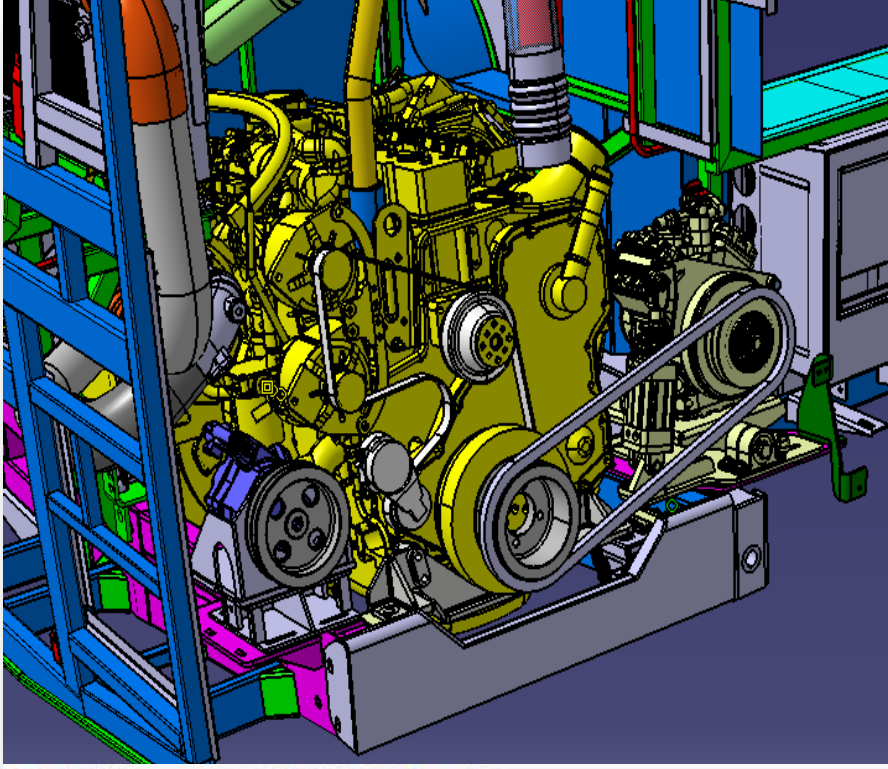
Motor beşiği şasi montaj bölgeleri
